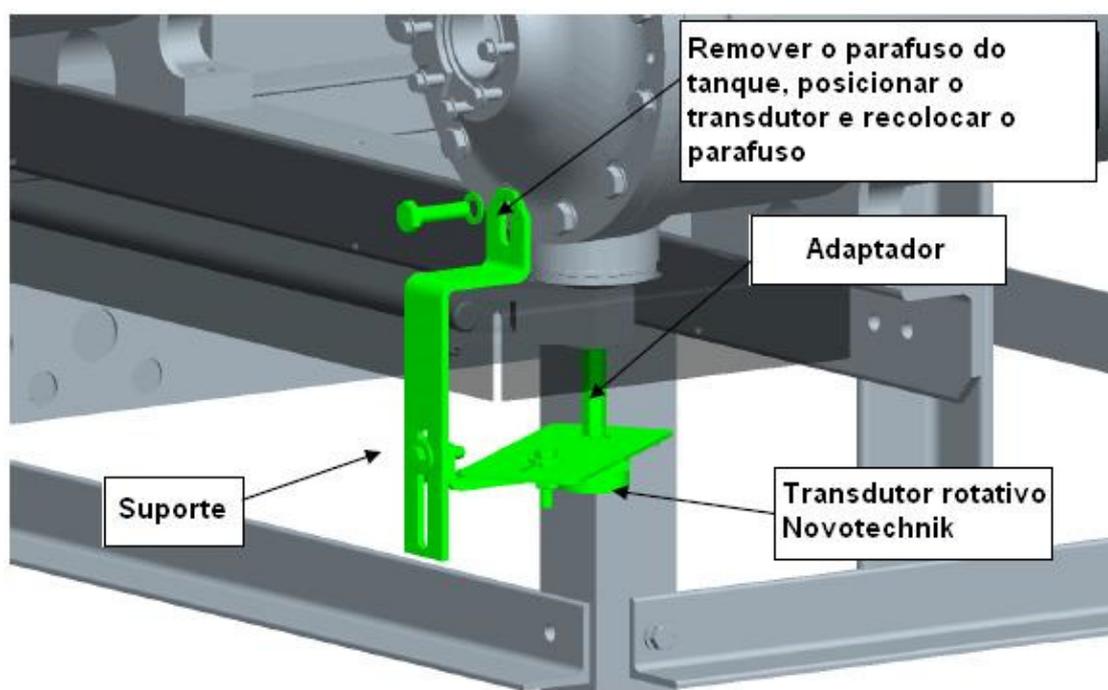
Montagem do Suporte do Transdutor Novotechnik na Tampa Final
